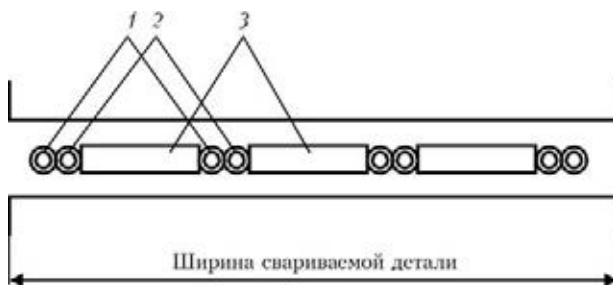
Схема плавящихся мундштуков с каналами для подачи проволоки (вариант на одну фазу): 1, 2 — каналы для перемещения сварочных проволок рабочих и дублирующих соответственно; 3 — пластины плавящегося мундштука
